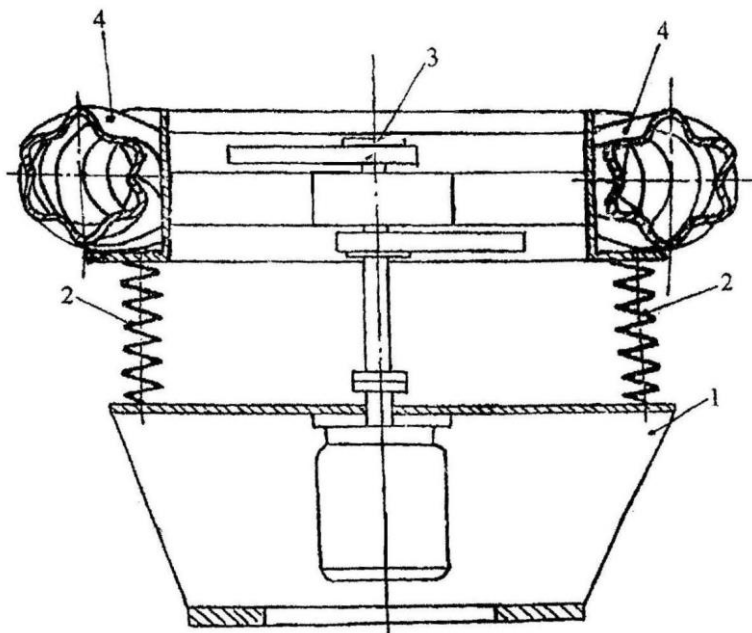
Виброустановка с тороидальной рабочей камерой.
